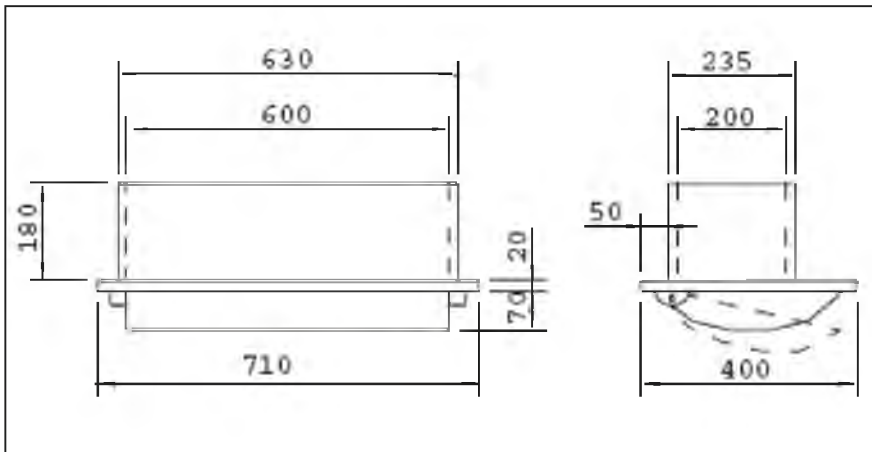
Габаритные размеры вентиля CL 30 S
